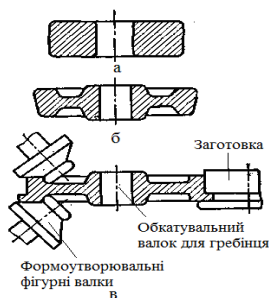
Схема отримання заготовки вагонного колеса: а – поковка; б – штампована поковка; в – розкатування
